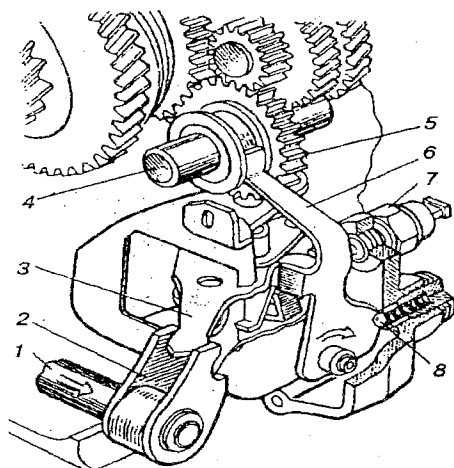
Механизм включения заднего хода коробки передач автомобиля ВАЗ-2110: 1 и 3 – соответственно шток и трехплечий рычаг выбора передач; 2 – рычаг штока выбора передач; 4 – ось промежуточной шестерни заднего хода; 5, 6 и 7 – соответственно промежуточная шестерня, вилка выключения передач и выключатель фонаря заднего хода; 8 – фиксатор вилки заднего хода
